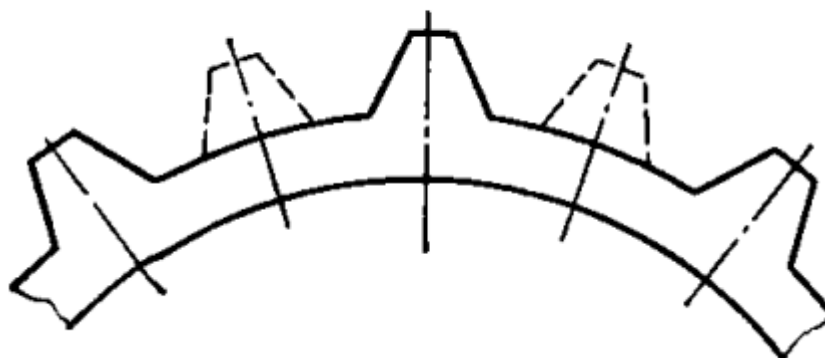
Зацепление зубьев гибкого и жесткого колес
